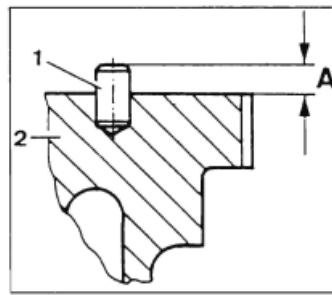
Фрагмент верхньої поверхні блока циліндрів із зазначенням розташування центрального штифта:
